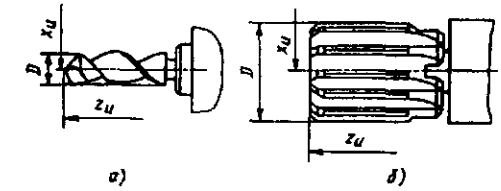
Примеры обозначения координат инструментов для станков с ЧПУ: а – для сверла; б – для развертки
